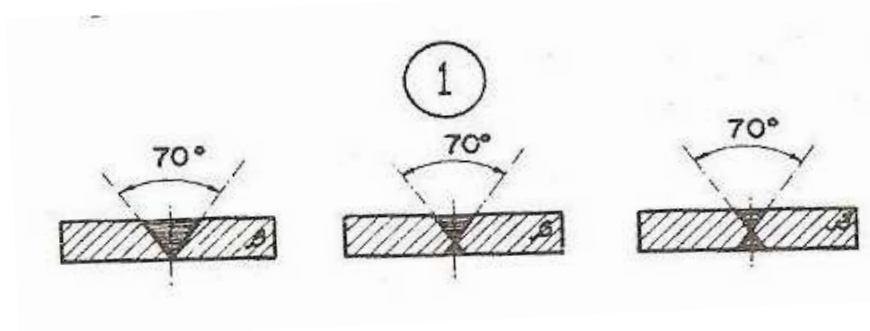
Tipos Soldadura en plano en forma de V-abierta, de V-cerrada.
